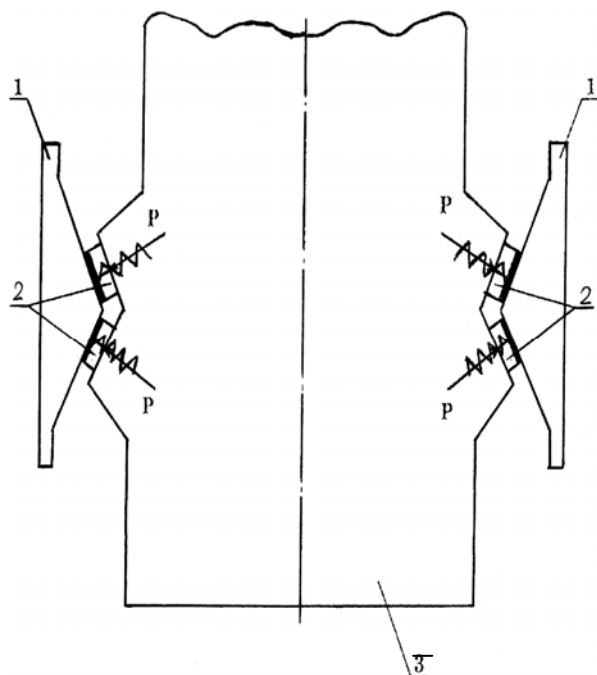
Связи между надрессорной балкой и боковинами (вид сверху):
